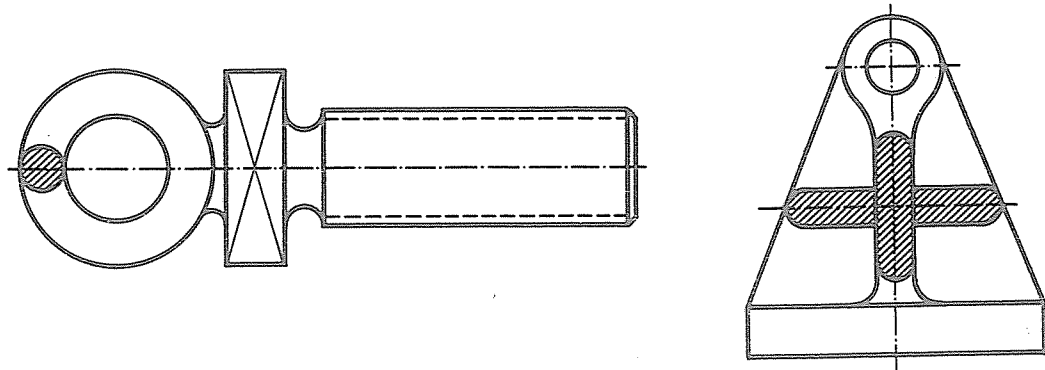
Ringschraube und Lagerbock mit eingezeichneten Querschnitten
